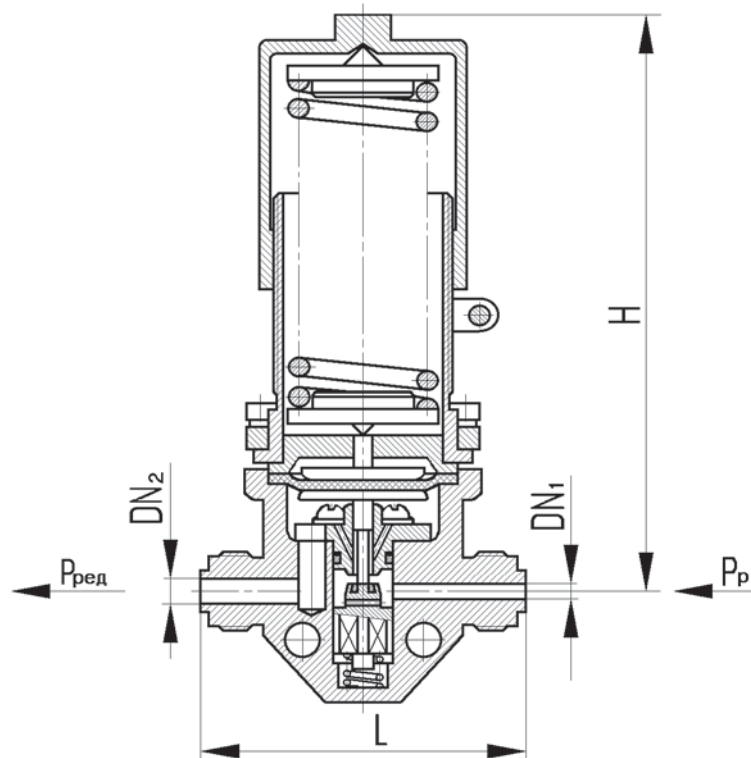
Клапан редуционный проходной штуцерный
